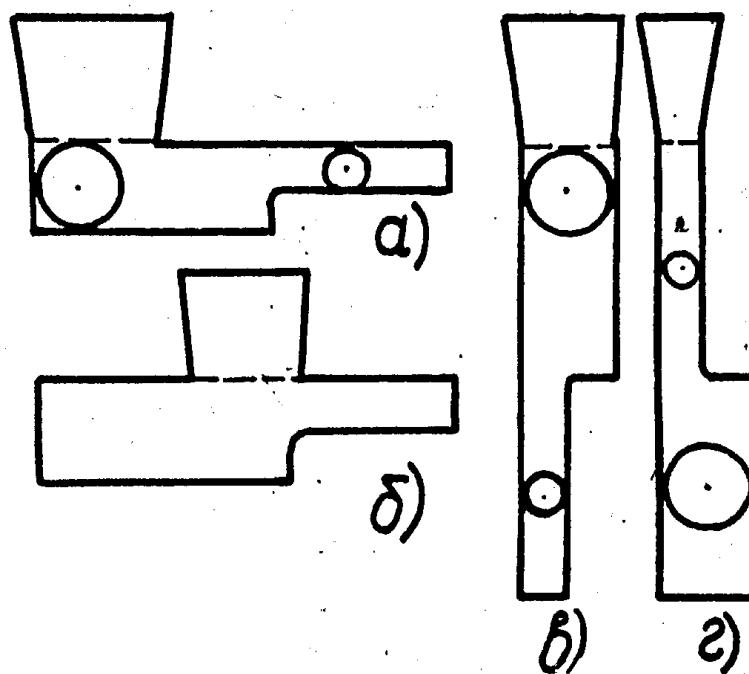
Отливки с резко изменяющейся толщиной стенки.
